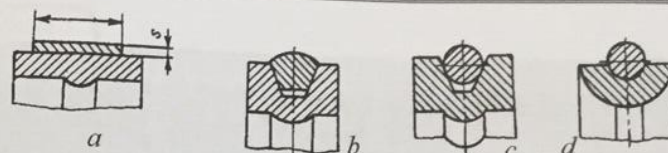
Clasificarea transmisiiilor după secțiunea elementului de tracțiune: a - elemente late; b - elemente trapezoidale; c, d - elemente rotunde.
